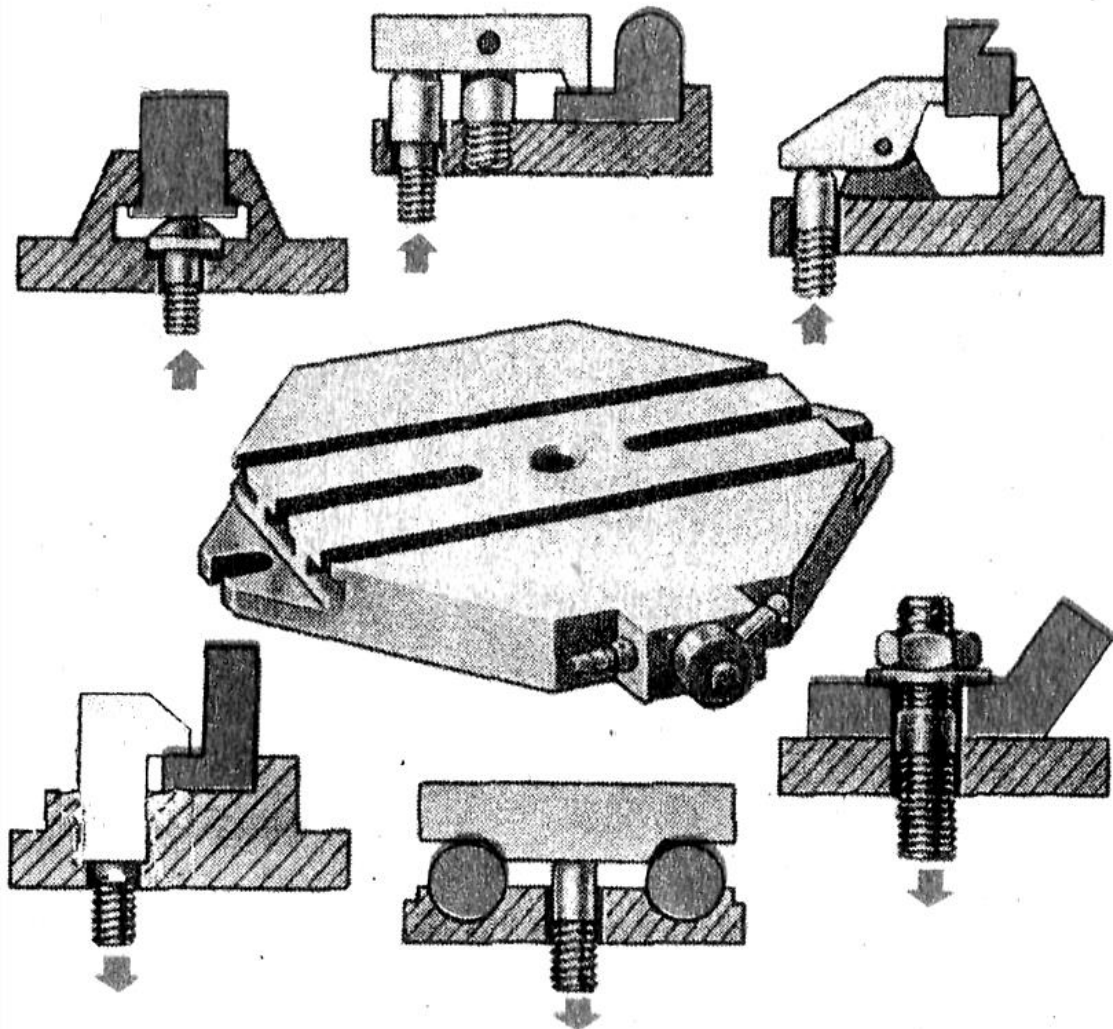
Схеми наладок для фіксації заготовки на за допомогою діафрагмового пневмоприводу
